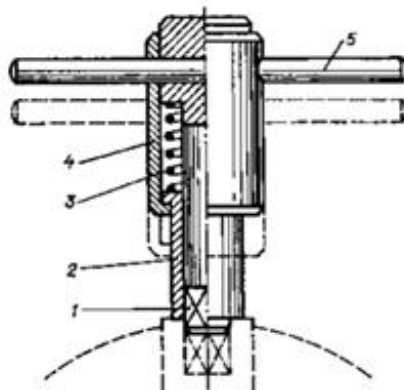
Самовідкидний ключ до патрона: 1) ключ; 2) втулка; 3) пружина; 4) корпус станка; 5) рукоятка
